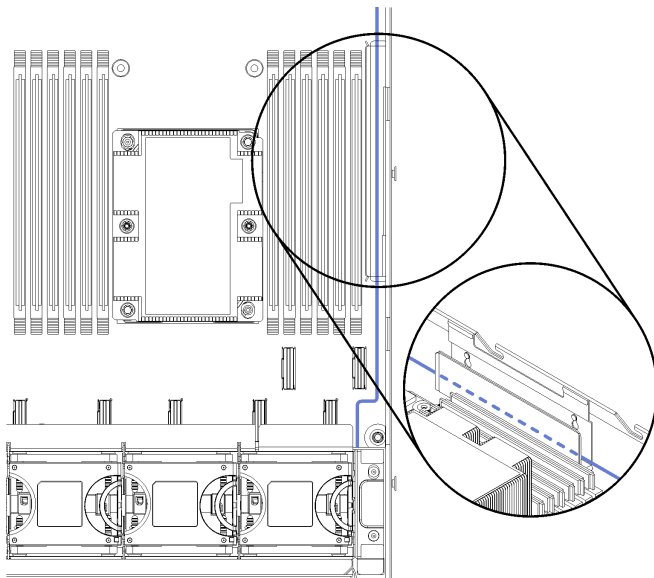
Instradamento dei cavi di alimentazione della ventola attraverso l'instradamento dei cavi destro
